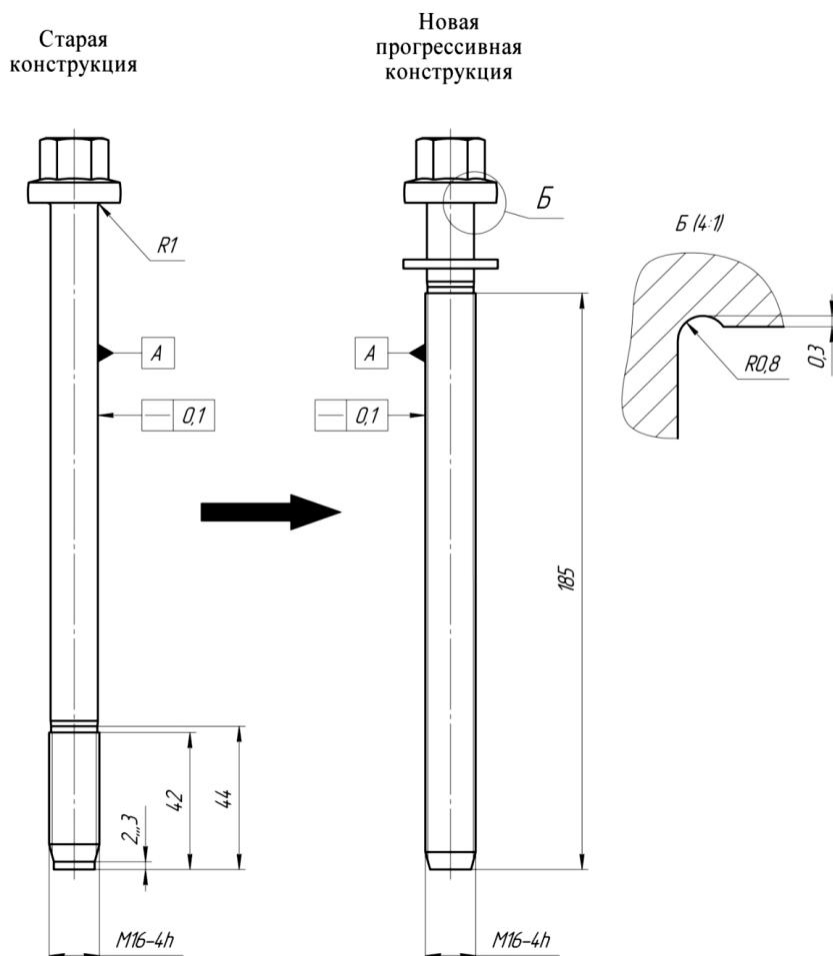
Конструкции фланцевого болта крепления головки блока цилиндров
